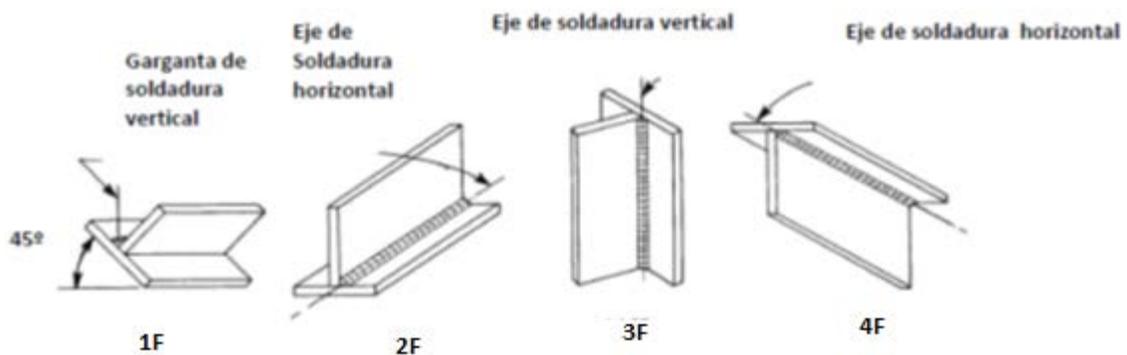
POSICIONES DE SOLDADURA DE FILETE
